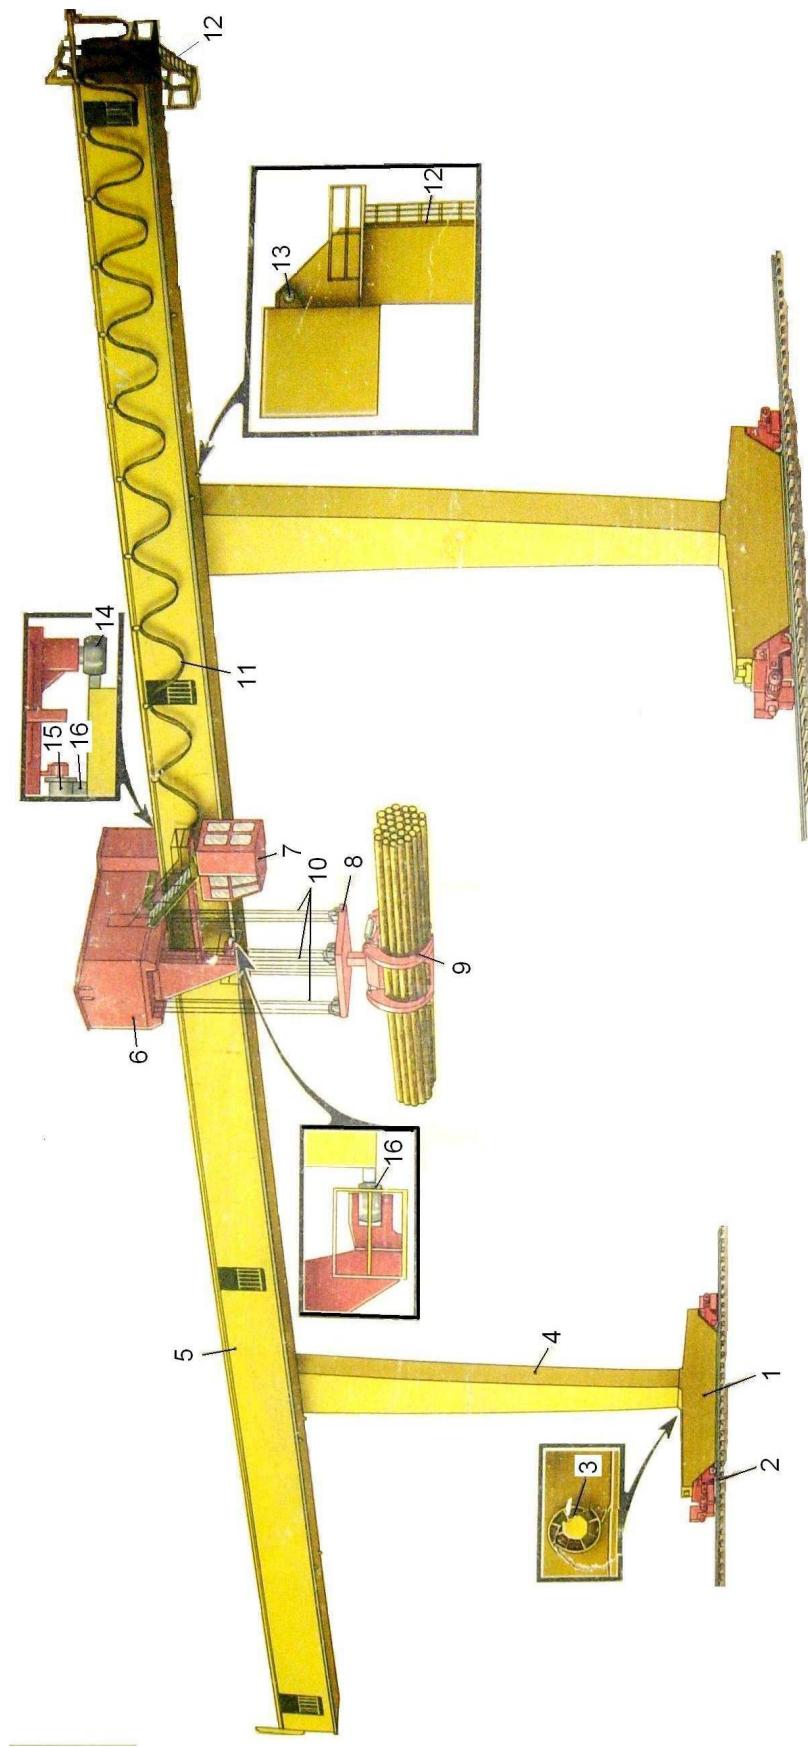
Консольно-козловой кран ККЛ-32: 1 – опорная балка, 2 – механизм передвижения крана, 3 – кабельный барабан, 4 – опора, 5 – пролетная балка, 6 – грузовая тележка, 7 – грейфер, 8 – подвеска, 9 – канат механизма подъёма груза, 10 – грейфер, 11 – узел токоподвода, 12 – лестница, 13 – шарнир опоры и пролетной балки, 14 – каток, 15 – опорный каток грузовой тележки, 16 – опорный рельс грузовой тележки
